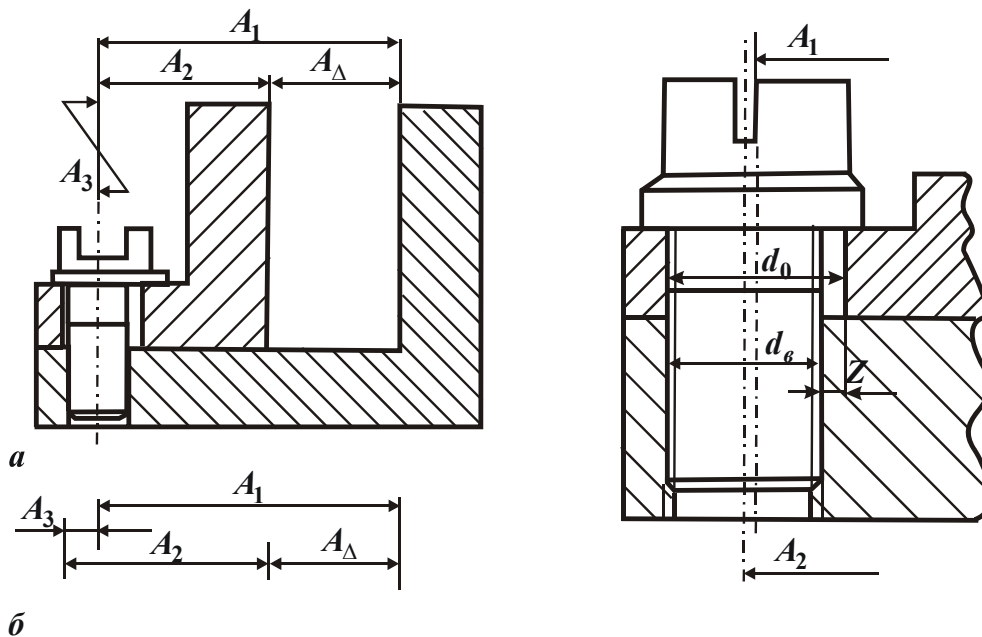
Схемы: а – конструкции компенсирующего звена, б – размерной цепи.
